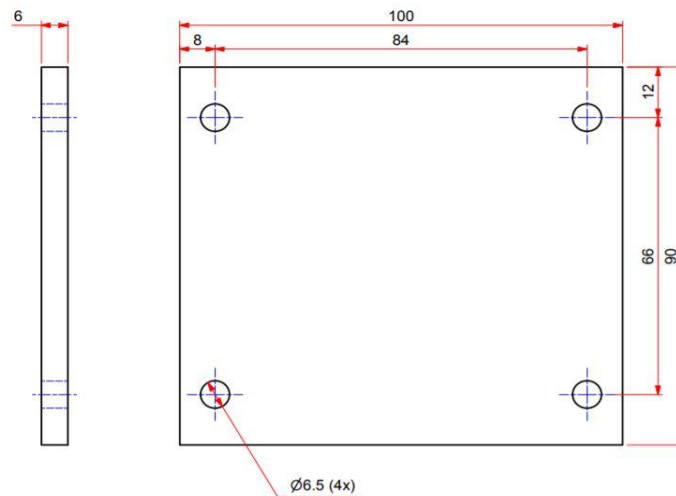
Detalhamento bidimensional do corpo de prova (dimensões em mm).
